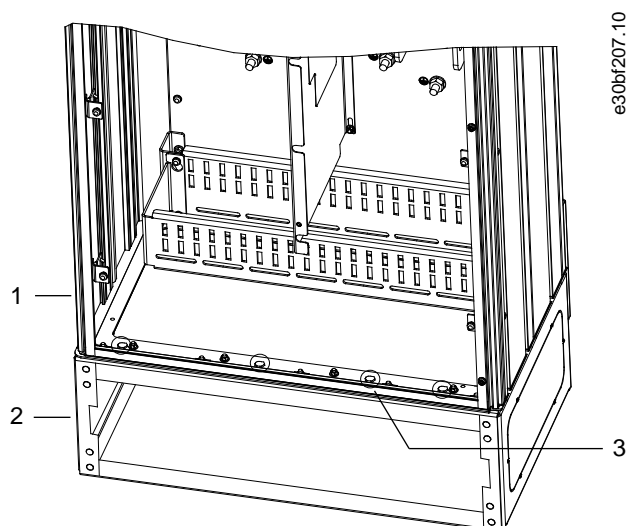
Montagepunkte für Befestigung des Gehäuses am Sockel
